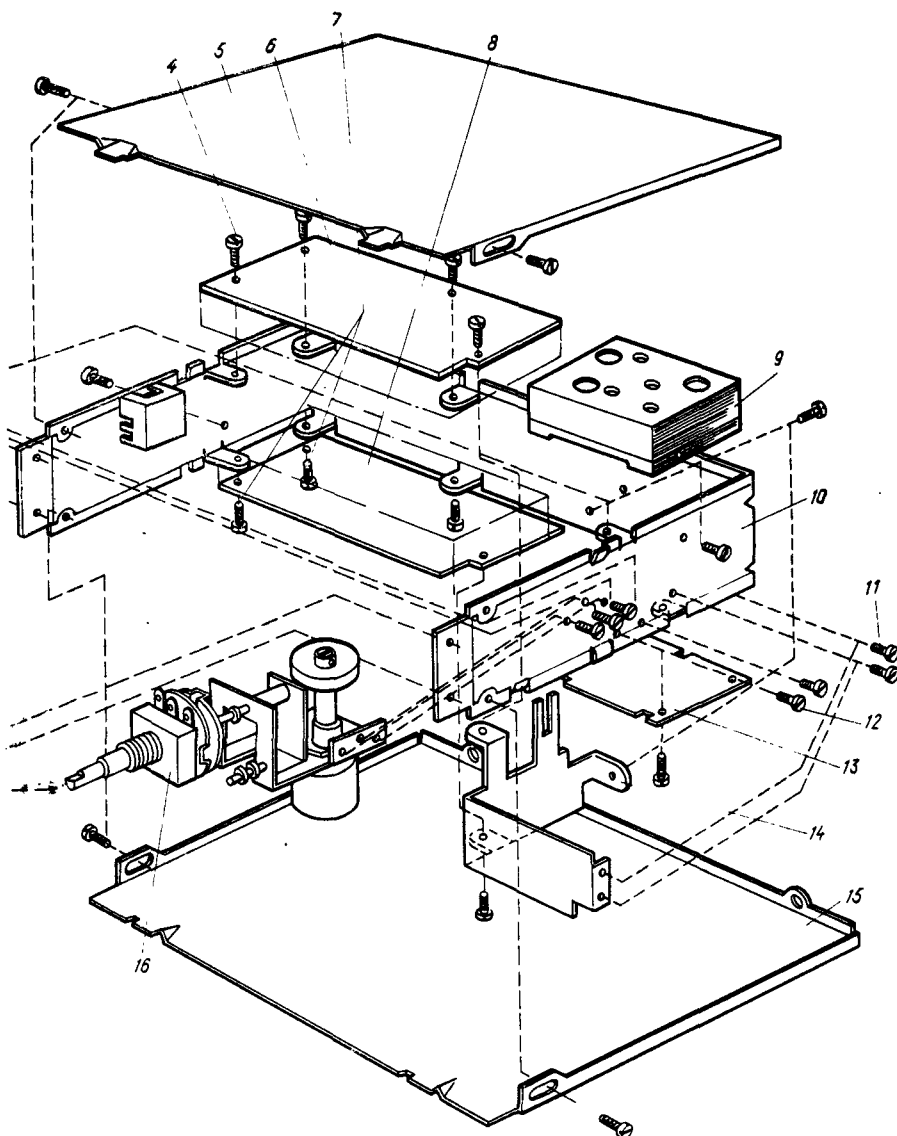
Схема разборки и сборки магнитолы «Эола-310-стерео»:
